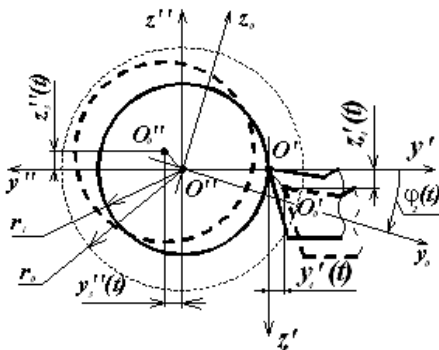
Схема формоутворення під час токарної обробки, де $O''O_0''$ — поточне положення осі деталі; $O'O_0'$ — поточне положення вершини інструменту; r_0 — радіус заготовки; r_1 — заданий радіус оброблюваної поверхні деталі
